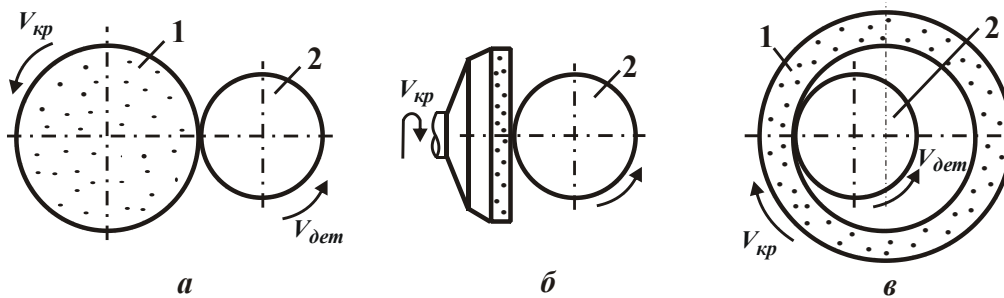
Кинематические схемы шлифования: 1 – круг; 2 – обрабатываемая деталь
